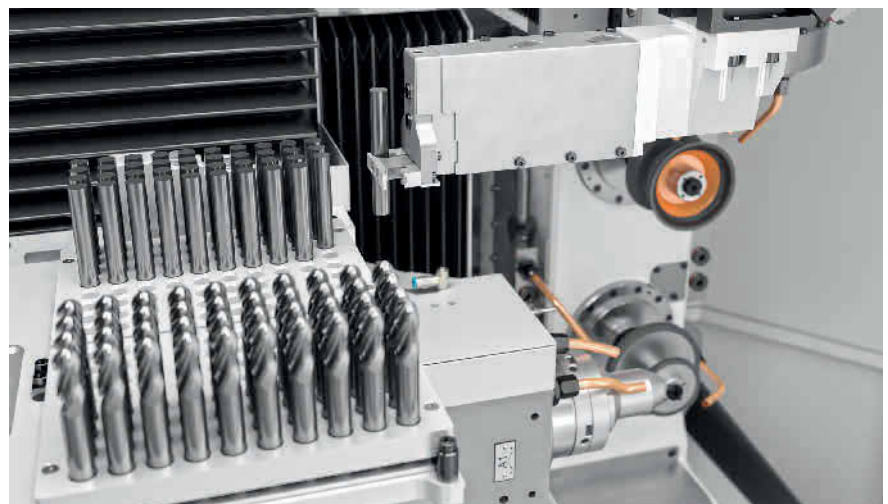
Interne Palettenlager bieten reichlich Platz für Schaftwerkzeuge. Foto: Vollmer
